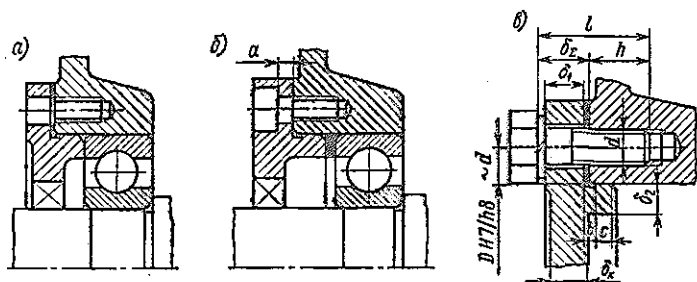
Конструкции винтовых крышек с отверстием для прохода вала
